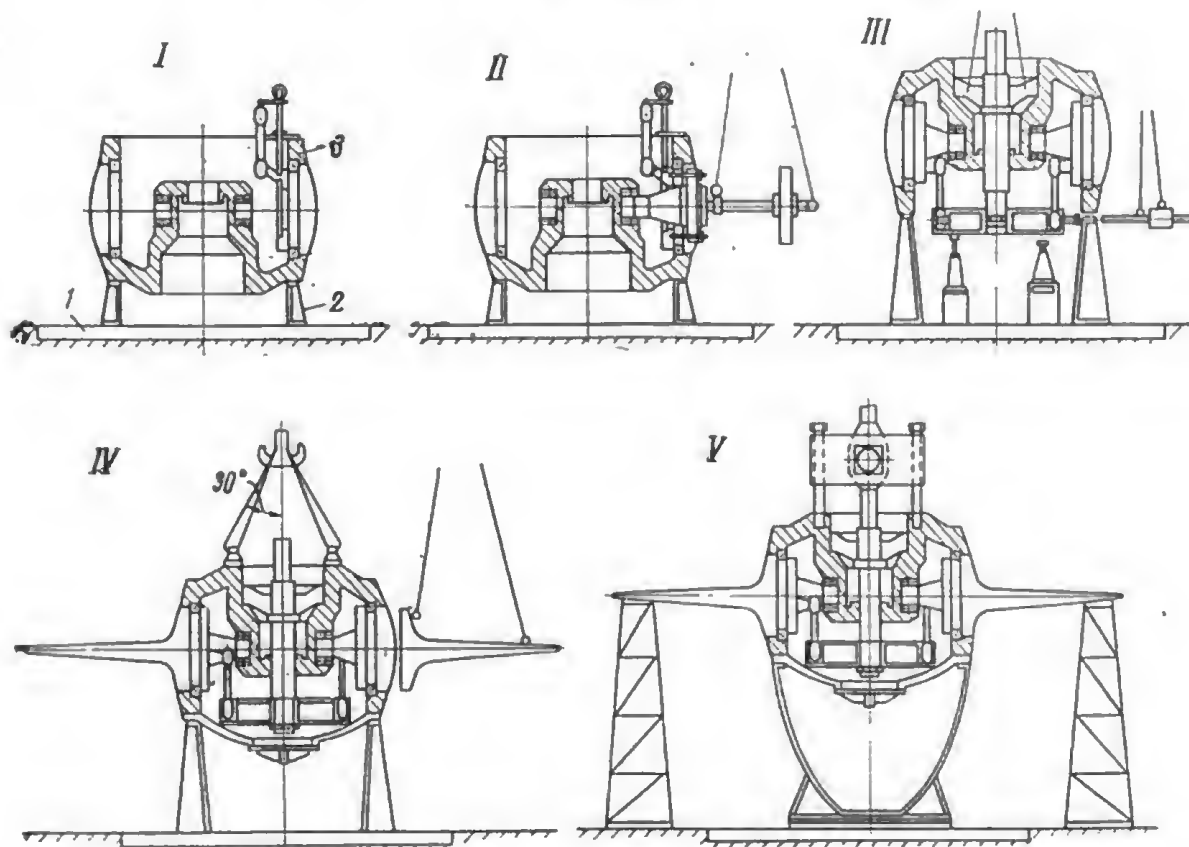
Схема сборки рабочего колеса крестовинного типа с кантовкой втулки.
